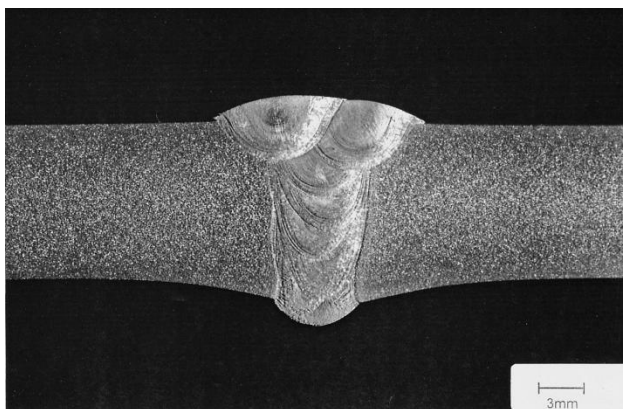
Ультразвуковой снимок профиля сварного шва
